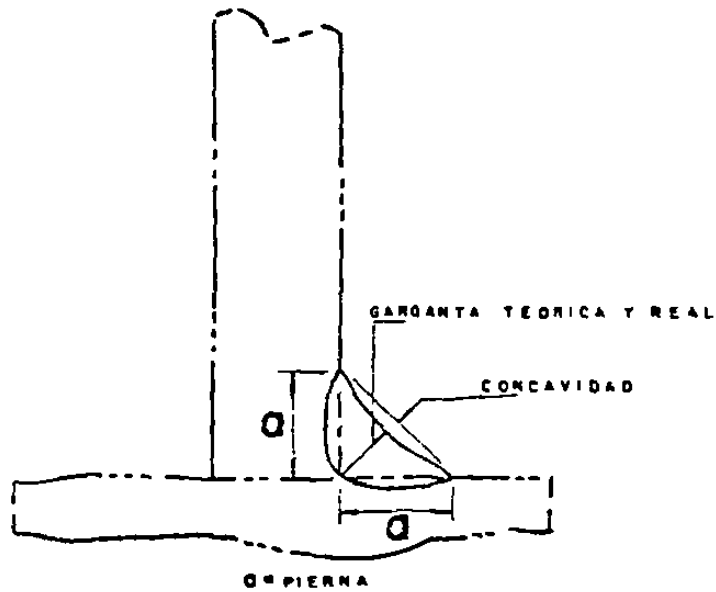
SOLDADURA DE FILETE CONCAVA
